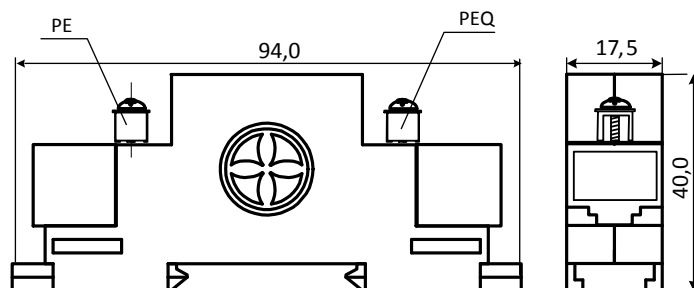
Габаритные размеры устройства Commeng FEP
